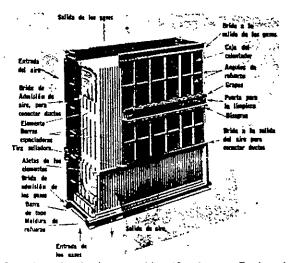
Precalentador de aire por celdas. (Combustion Engineering)
